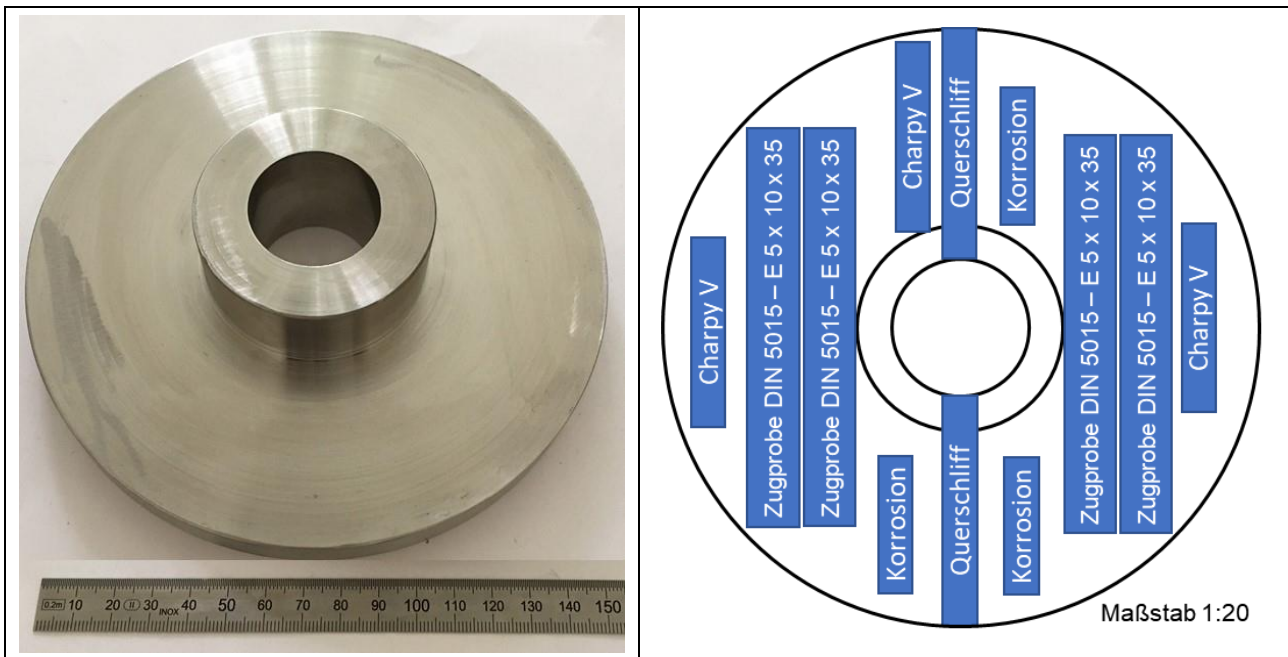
Bearbeiteter Flansch und Probenentnahmeplan
